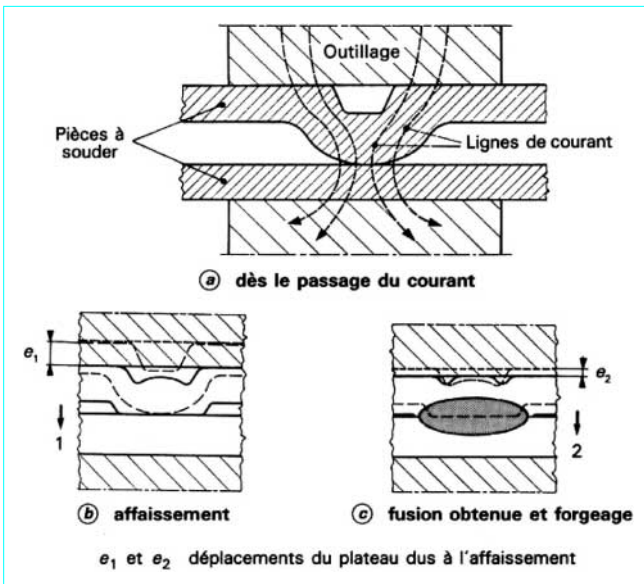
Soudage par bossages : formation de la soudure
